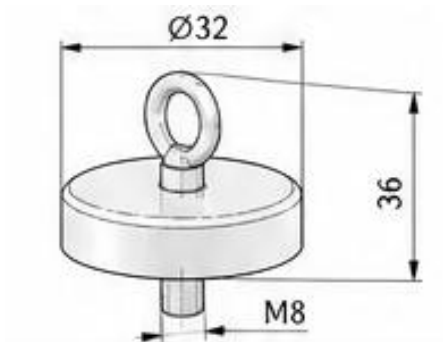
Робоче креслення магнітного фіксатора контрольного пристосування
